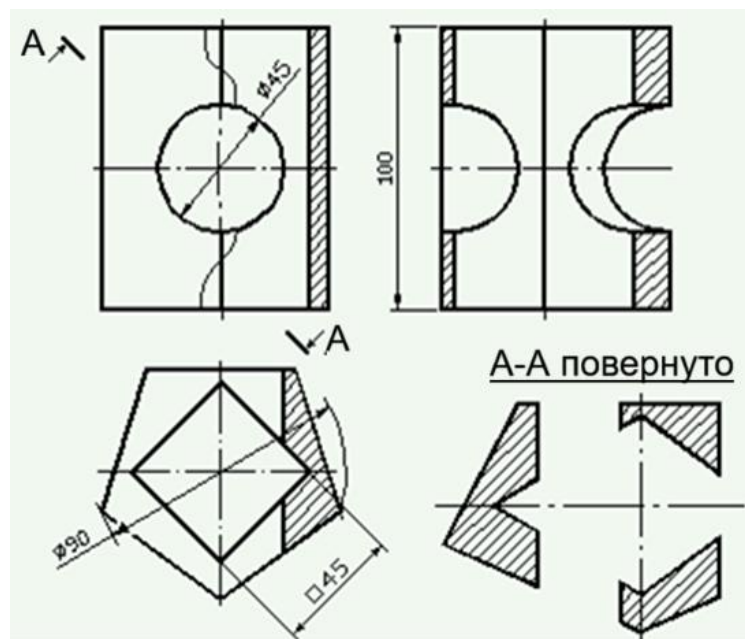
Остаточний вигляд креслення вихідної деталі
